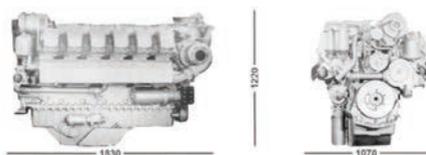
Габаритные размеры дизельного двигателя ЯМЗ - 847.10
